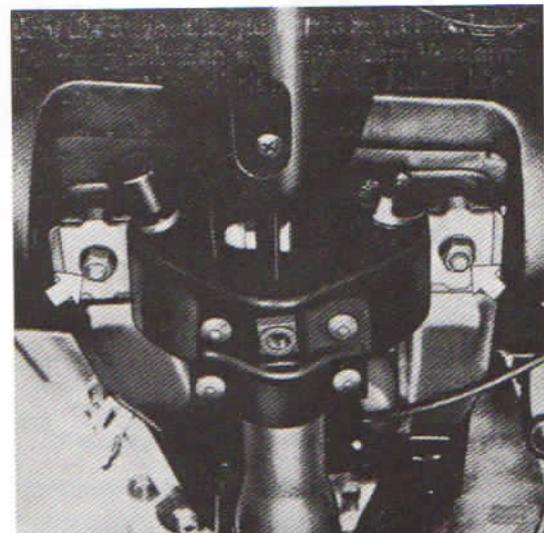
Beide Muttern für vordere Abreißschlittenbefestigung abschrauben
